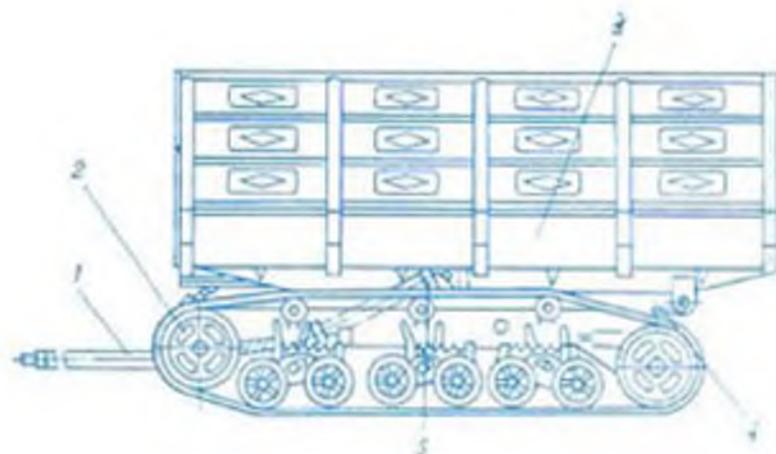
Прицепы. Гусеничный прицеп-самосвал МТП-24Б: 1 — прицепное устройство; 2 — гусеничный ход; 3 — платформа с бортами; 4 — рама; 5 — телескопический гидроцилиндр.
